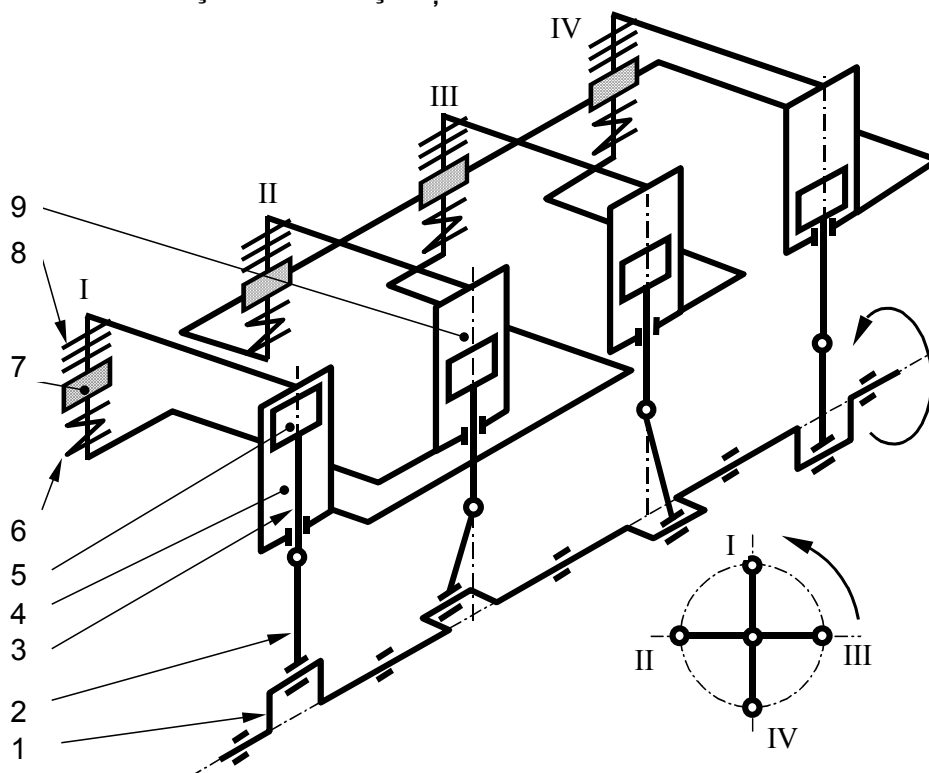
Motor Stirling cu pistoane cu dublă acțiune cu patru cilindri în linie: 1 - arbore cu patru coturi; 2 - bielă; 3 - tija pistonului; 4 - cameră de comprimare; 5 - piston cu dublu efect; 6 - răcitor; 7 - regenerator; 8 - încălzitor; 9 - cameră de destindere;
